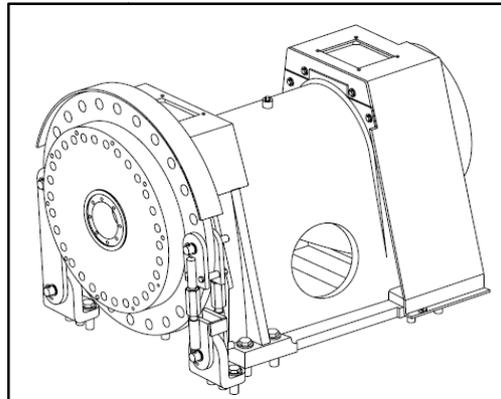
Système de blocage rotor de la machine G5X [10].
